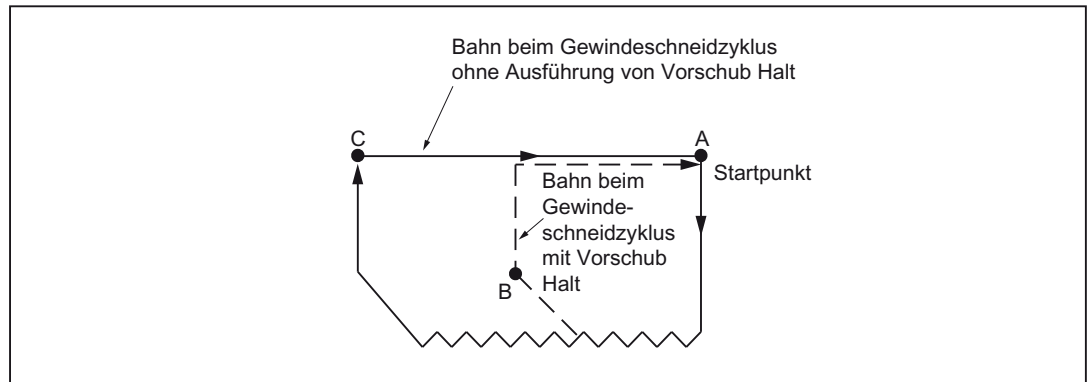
Vorschub Halt während der Ausführung des Gewindeschneidzyklus
